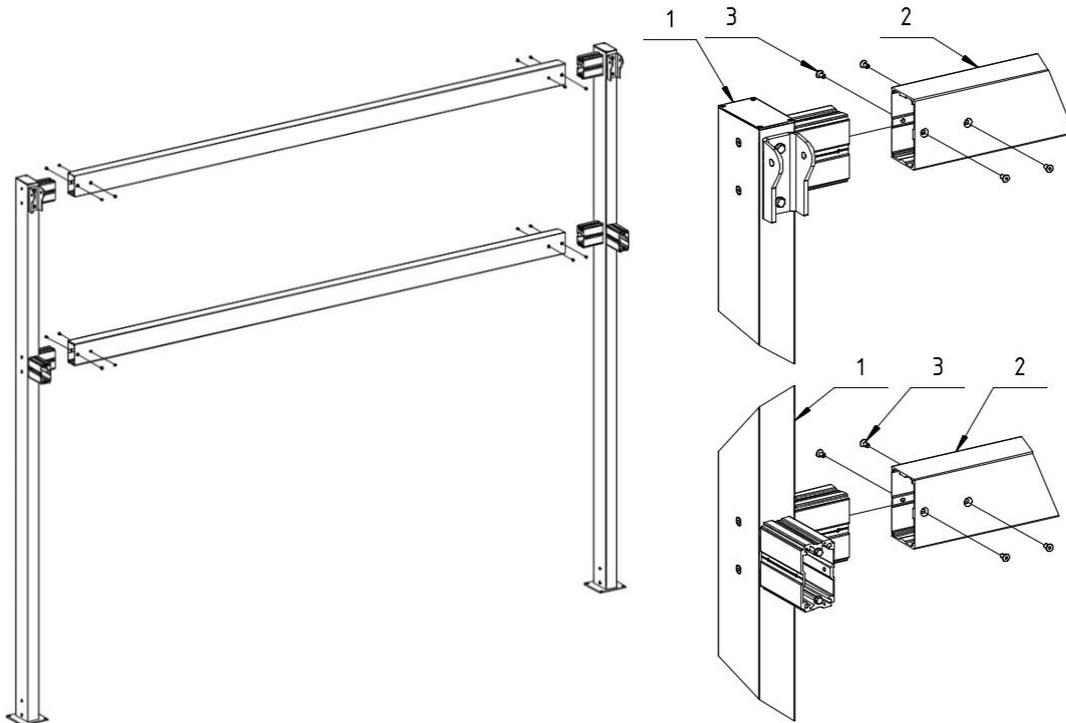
Manière de montage de la barre d'arrière 1 - Poteau haut, 2 - Barre d'arrière, 3 - Vis M8x16.
